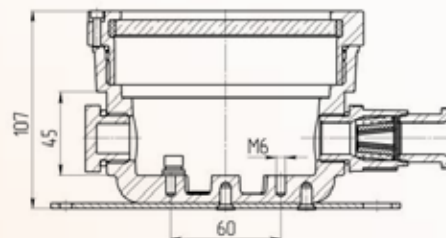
Внутренние, габаритные и установочные размеры коробки
